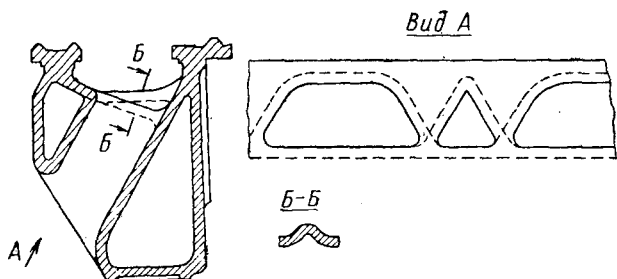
Сечение станины станка V3R фирмы «VDF»
